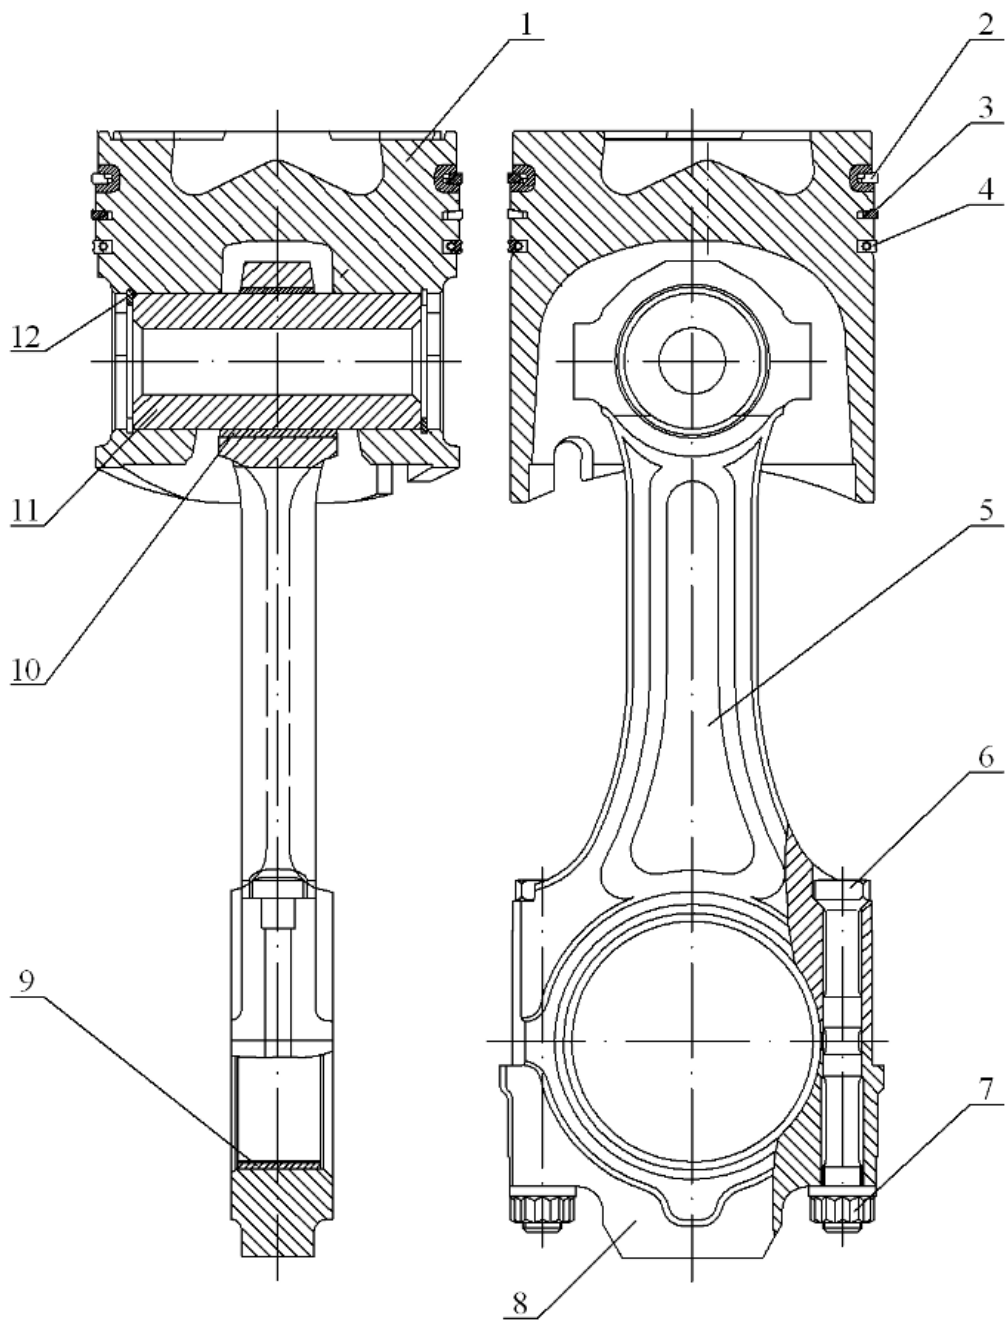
Поршень с кольцами в сборе с шатуном:
